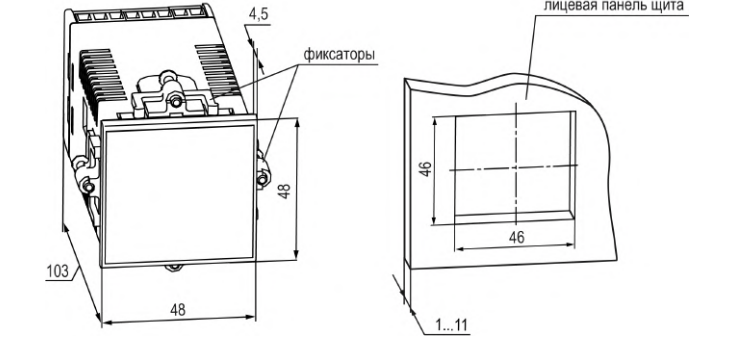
Габаритные размеры корпуса Щ5 и монтажного отверстия в щите
